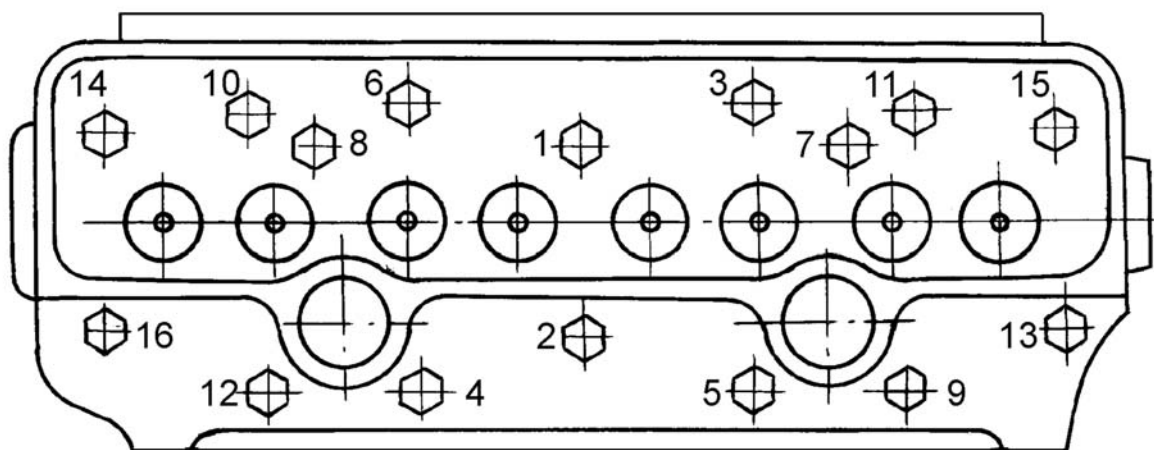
Порядок затяжки болтов крепления головки блока цилиндров
